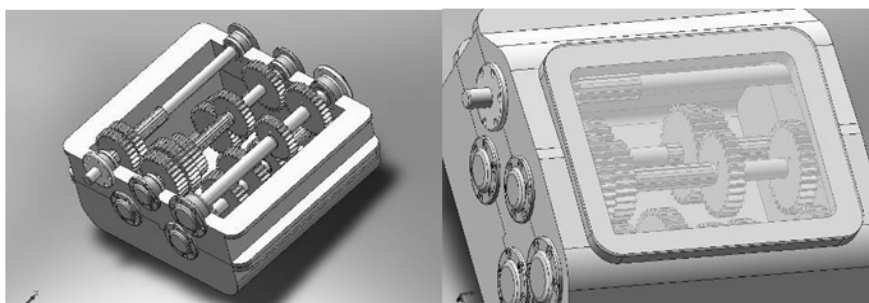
Коробка скоростей металлорежущего станка 6М82
